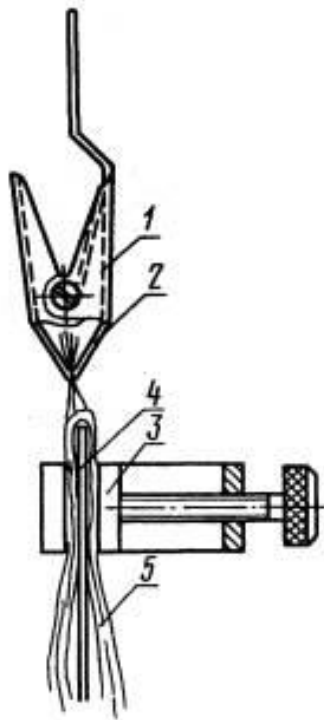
Приспособление для захвата пучков волокон. 1 - верхний зажим; 2 - губки верхнего зажима; 3 - тиски; 4 - планка; 5 – проба
